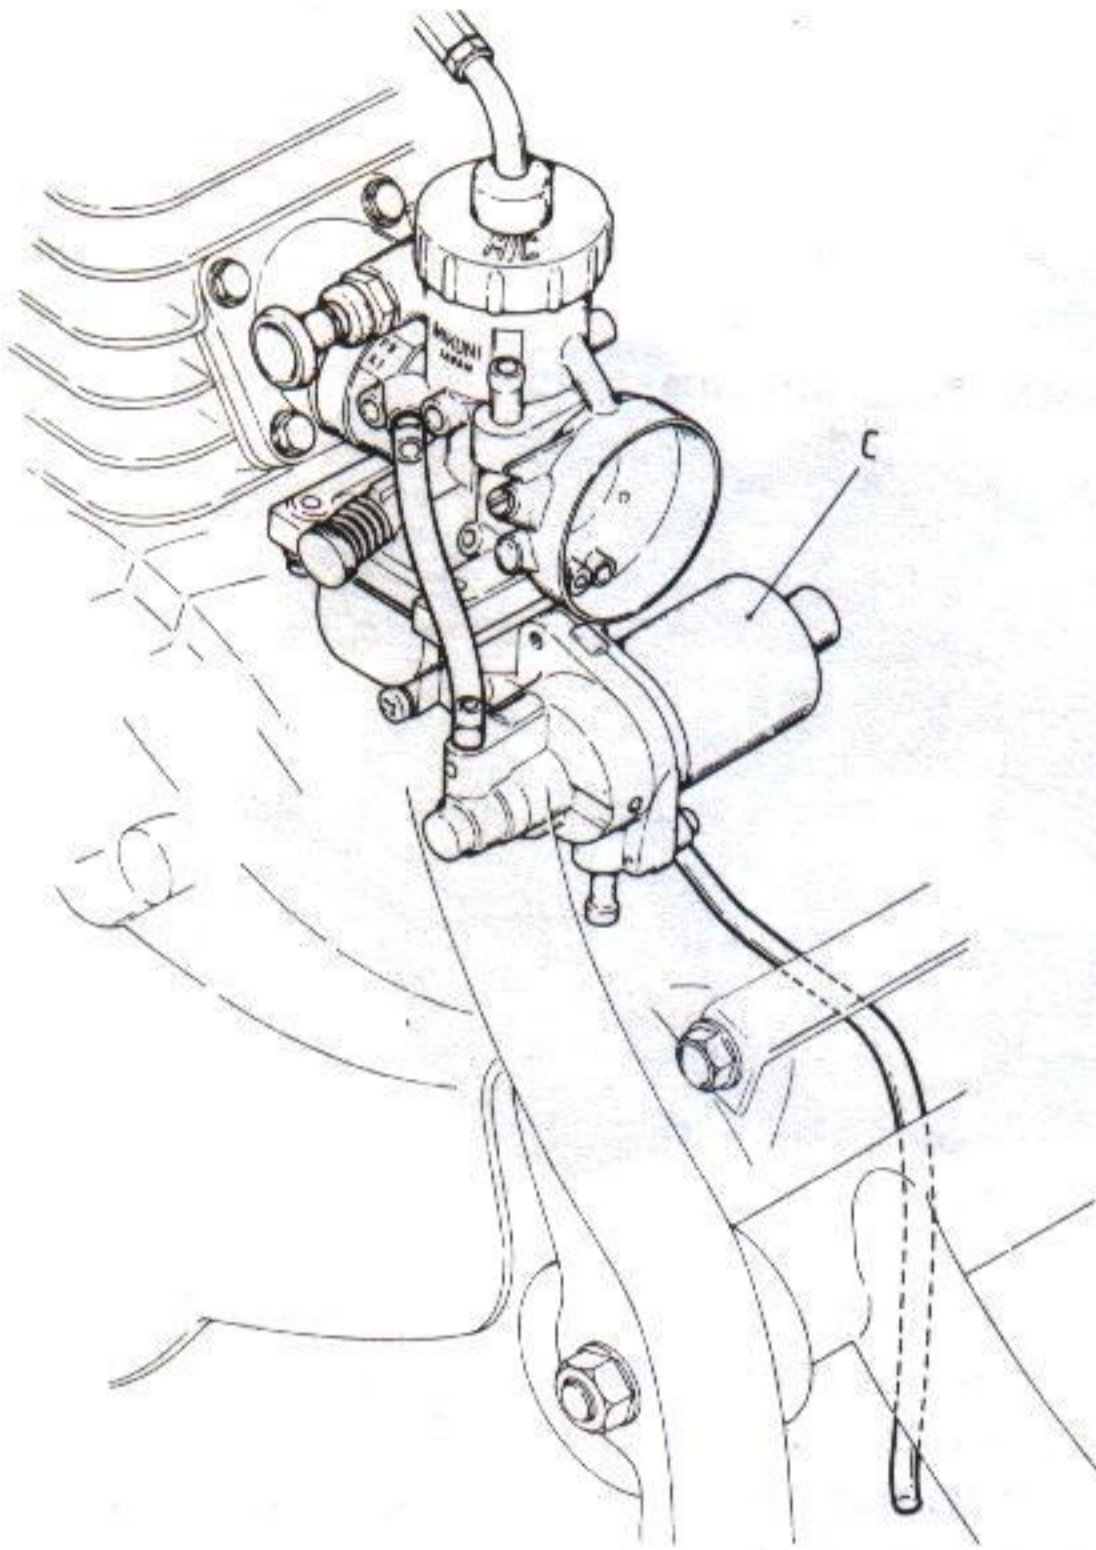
Carburador de moto más-trando en C su cápsula altimétrica.
